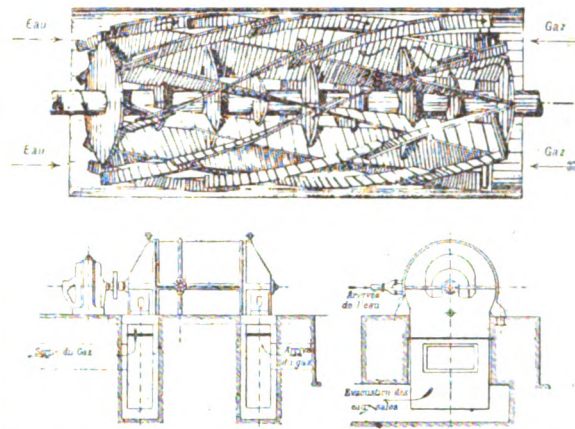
, 5 et 6. — Vue intérieure et ensemble d'un épurateur centrifuge axial Flössel.
